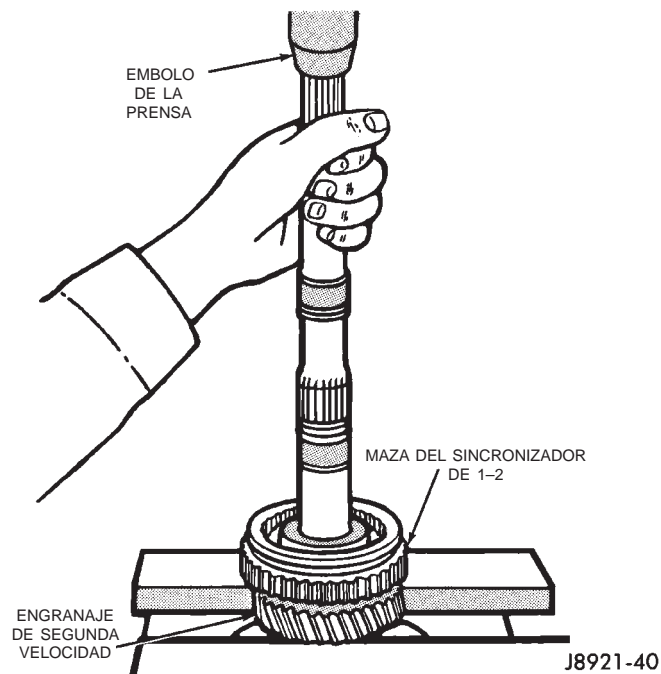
Desmontaje del sincronizador 1-2, el engranaje de marcha atrás y el engranaje de segunda velocidad
